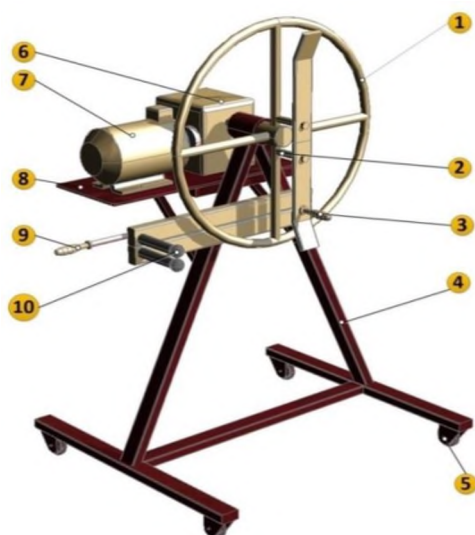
Модернизированный станок для скатки и перекатки пожарных напорных рукавов на новое ребро ТЦ-11П: 1 – колесо со спицами; 2 – штырь со съемной втулкой и прижимом; 3 – рукоятка; 4 – рама сварная; 5 – колесо (ролик); 6 – редуктор червячный; 7 – электродвигатель; 8 – кронштейн; 9 – рычаг подвижный; 10 – ригели направляющие
